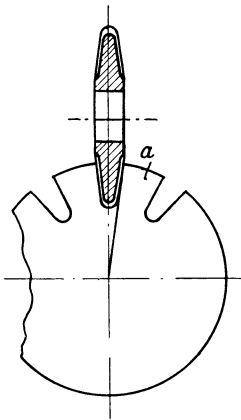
Das Fräsen der Nuten für hinterdrehte Fräser.
